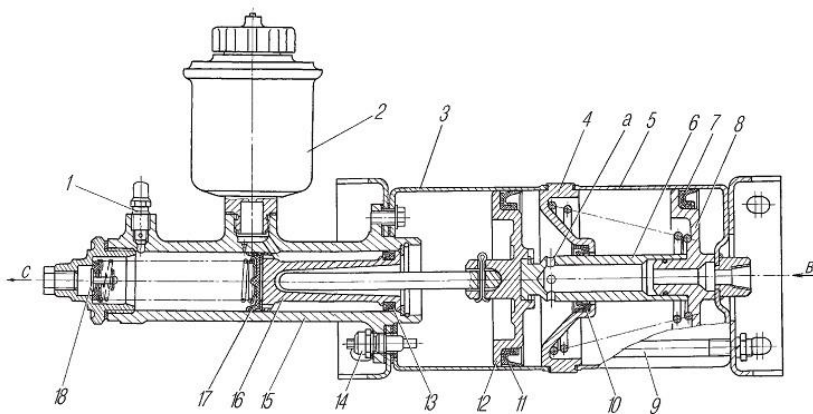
Пневматический усилитель с главным тормозным цилиндром автомобиля «Урал»:
